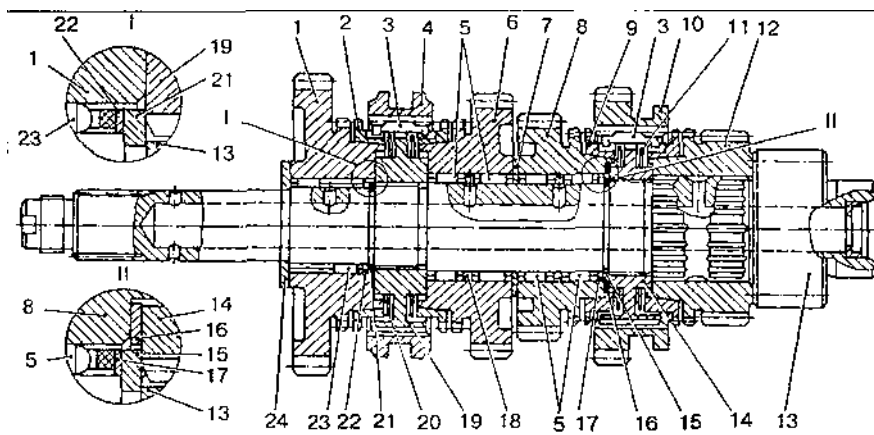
Ведущая шестерня главной передачи: 1, 6, 8, 12 — шестерни ведомые первой, второй, третьей и четвертой передач; 2, 9 — кольца, блокирующие синхронизаторы первой-второй и третьей-четвертой передач; 3 — сухарь синхронизатора; 4 — муфта включения синхронизатора первой и второй передач; 5 — подшипники ведомых шестерен второй и третьей передач; 7, 16 — шайбы упорные; 10 — шестерня ведомая заднего хода; 11, 20 — пружины синхронизатора третьей-четвертой и первой-второй передач; 13 — шестерня ведущая главной передачи; 14, 19 — ступицы муфт переключения третьей-четвертой и первой-второй передач; 15, 21 — кольца стопорные; 17, 22 — кольца; 18 — проставочное кольцо; 23 — подшипник ведомой шестерни первой передачи; 24 — шайба упорная.
